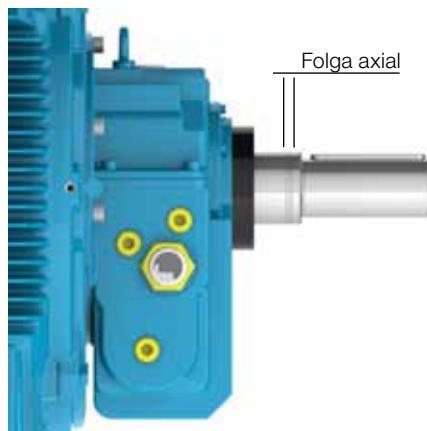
Folga axial em motor equipado com mancal de deslizamento.
